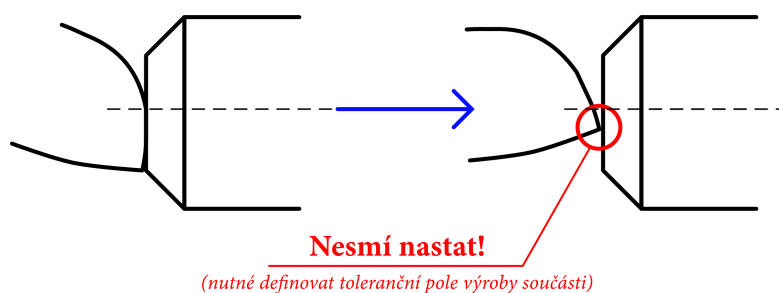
Kleštinový mechanismus pro axiální zajištění
